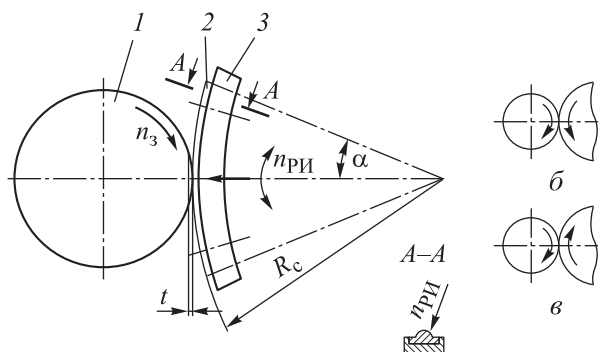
Схемы маятникового ППД: а — кинематическая; б и в — качения и скольжения в зоне контакта заготовки и РИ
